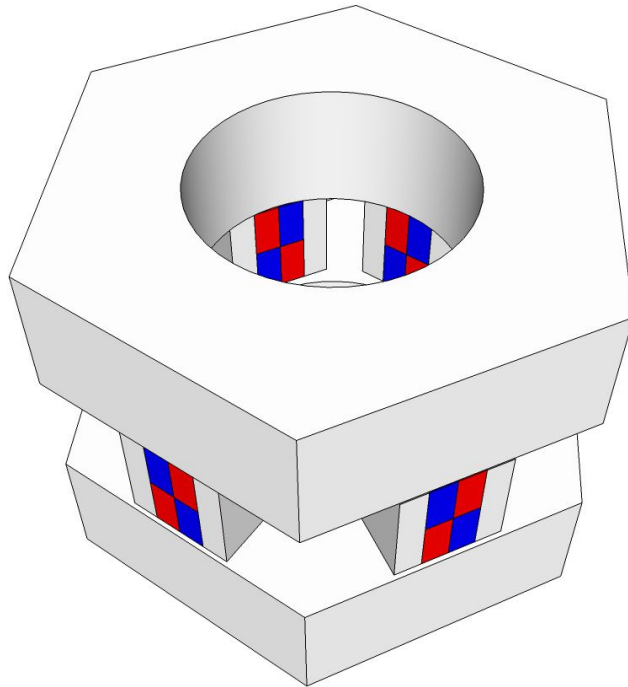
Magnetická tělesa rotoru ve tvaru „soudku“
